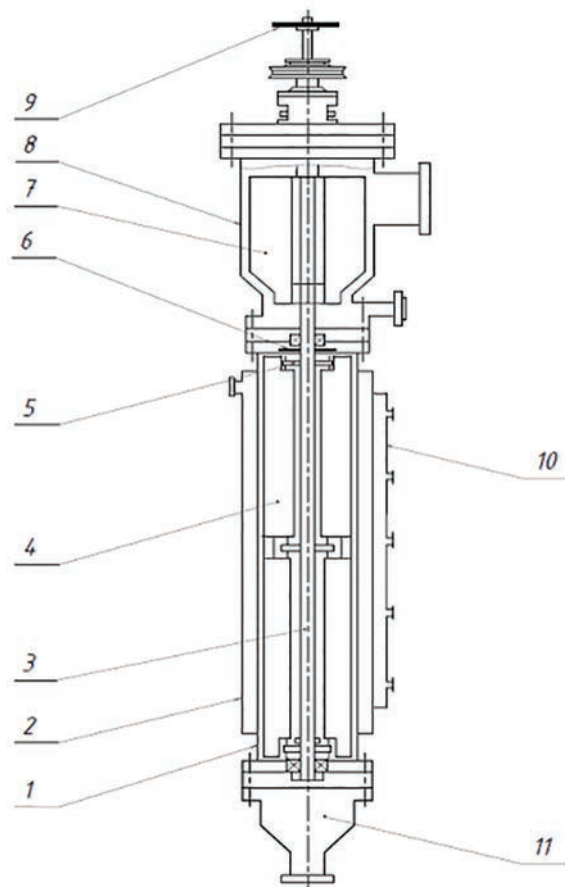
Схема роторного плівкового апарата з шарнірним кріпленням лопатей: 1 – корпус; 2 – нагрівальна сорочка; 3 – вал ротора; 4 – лопаті; 5 – маточина; 6 – розподільче кільце; 7 – робоче колесо; 8 – сепаратор; 9 – датчик тахометра; 10 – термоелементи; 11 – днище
